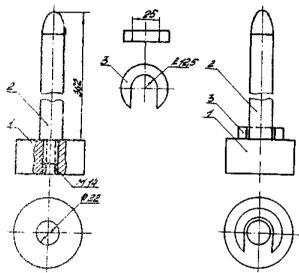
Приспособление (ПІ) для проверки усилия вытягивания подвижного контакта из неподвижного розеточного контакта: 1 - контрольный груз (P=800 H); 2 - контрольный стержень; 3 - контрольный груз (P=20H)
